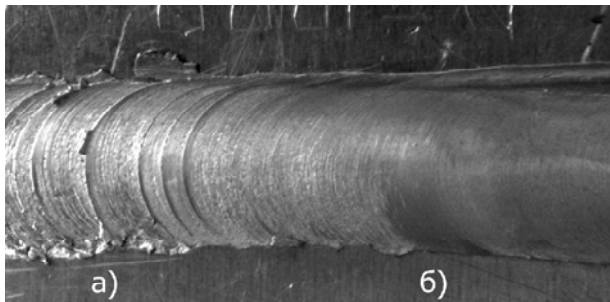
Зовнішній вигляд поверхні зварного шва залежно від умов роботи інструмента:
